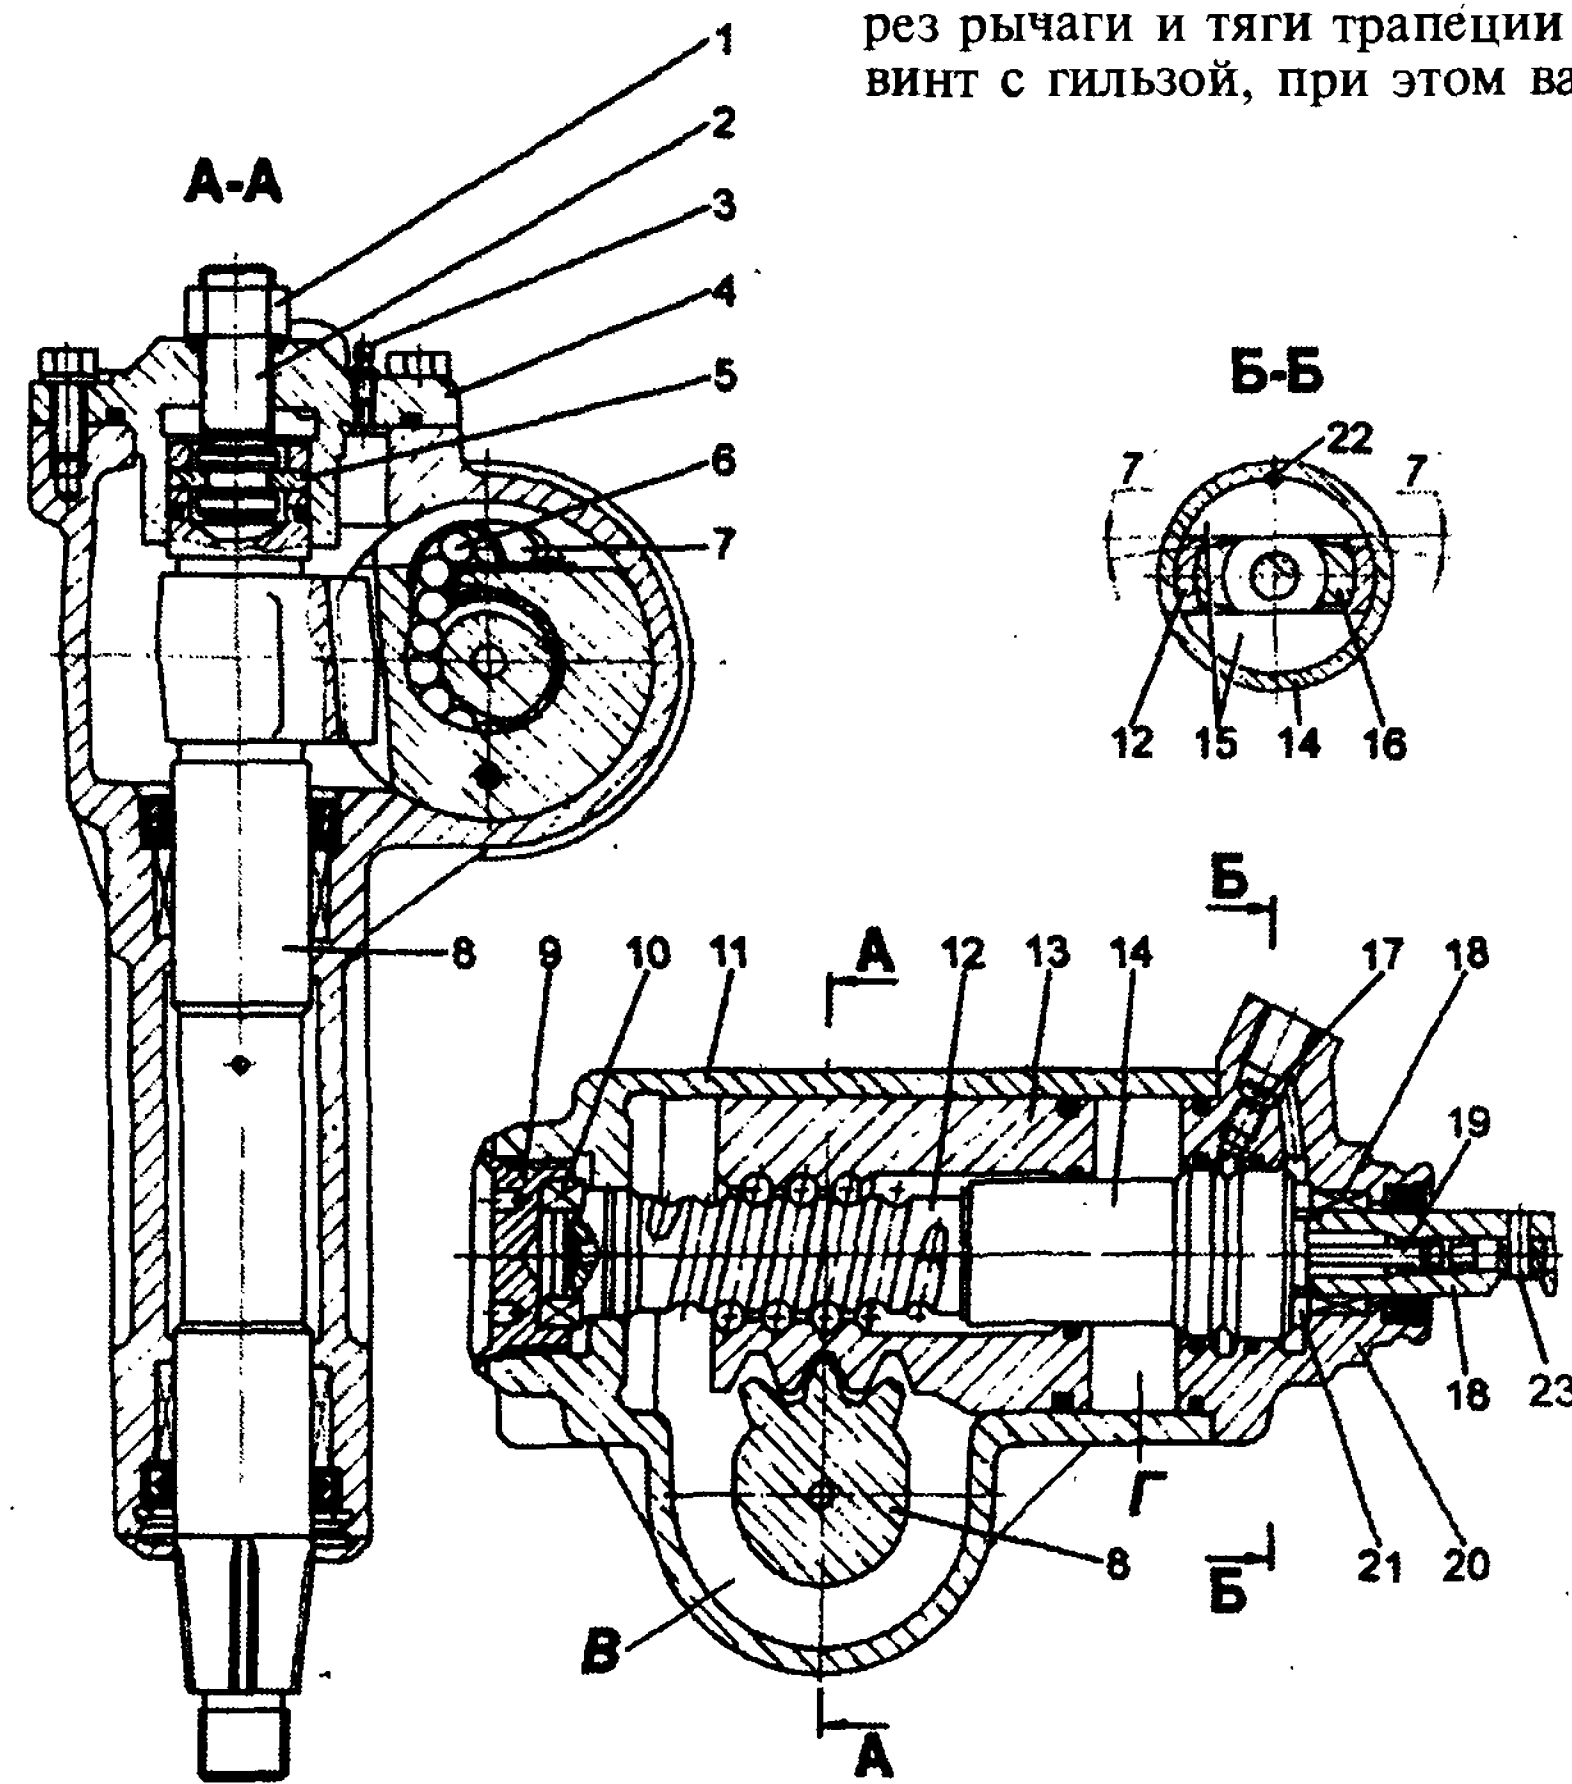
Интегральный рулевой механизм: В и Г- полости; 1 - контргайка; 2 - регулировочный винт; 3 - клапан прокачки; 4 - крышка боковая; 5 - шайба; 6 - шарик; 7 - желоб; 8 - вал сошки; 9 - гайка; 10 и 21 - подшипники винта; 11 - картер; 12 - винт рулевого управления; 13 - гайка-поршень; 14 - гильза; 15 - упоры; 16 - вал-золотник; 17 - перепускной клапан; 18 - роликовый подшипник; 19 - торсион; 20 - корпус распределителя; 22 - ролик; 23 - штифт
